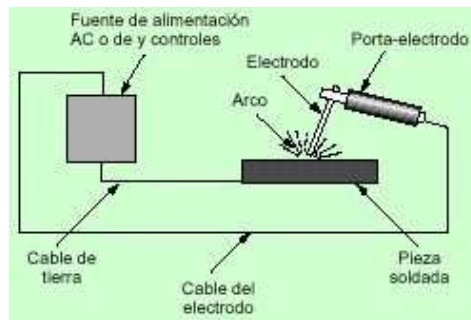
Esquema del proceso de soldadura eléctrica al arco
